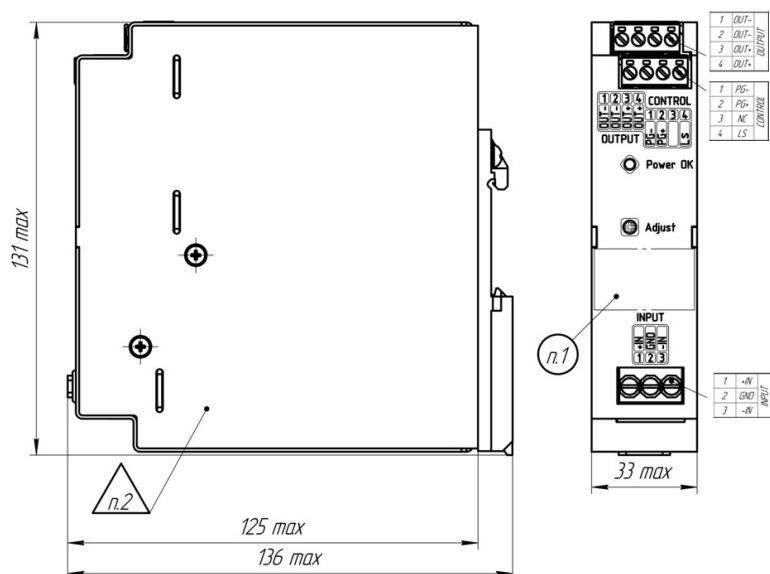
Габаритный чертеж для исполнения VDD75TND.
